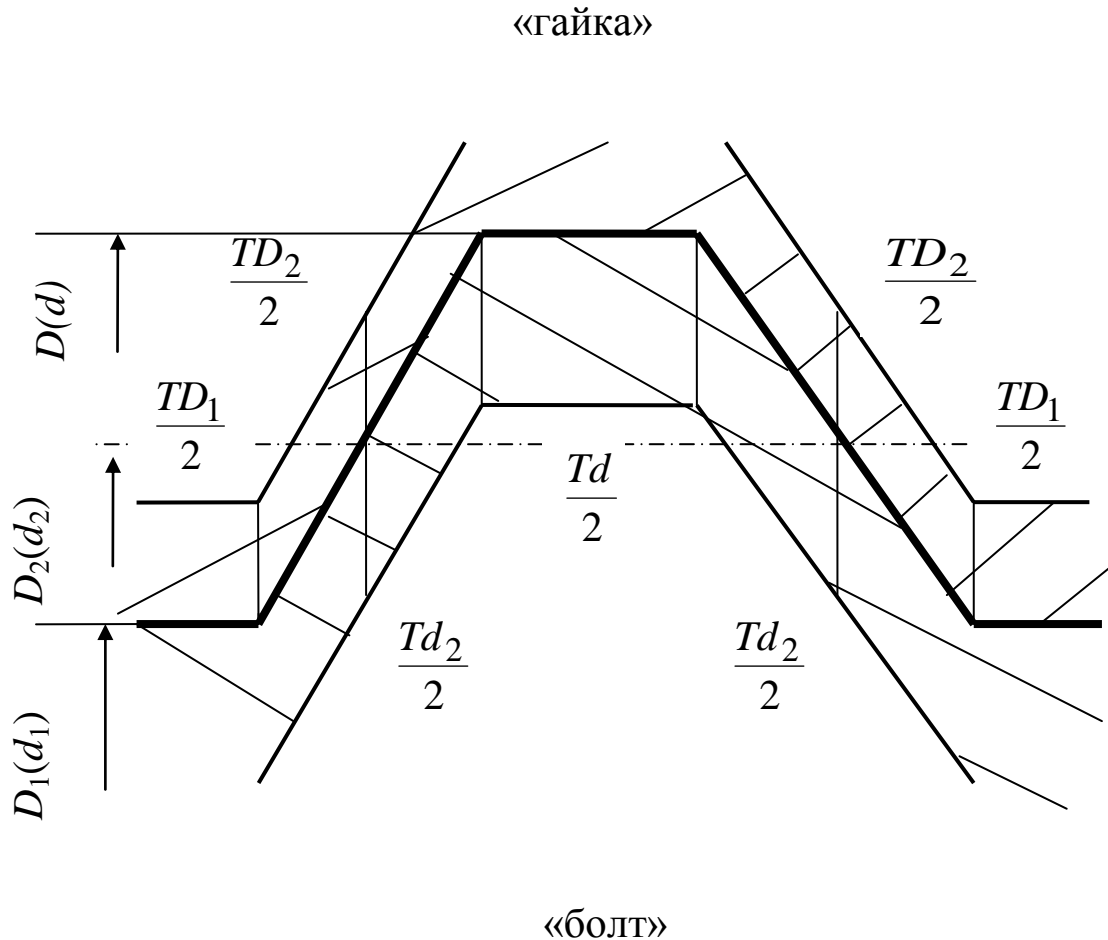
Предельные контуры резьбового соединения метрической резьбы
